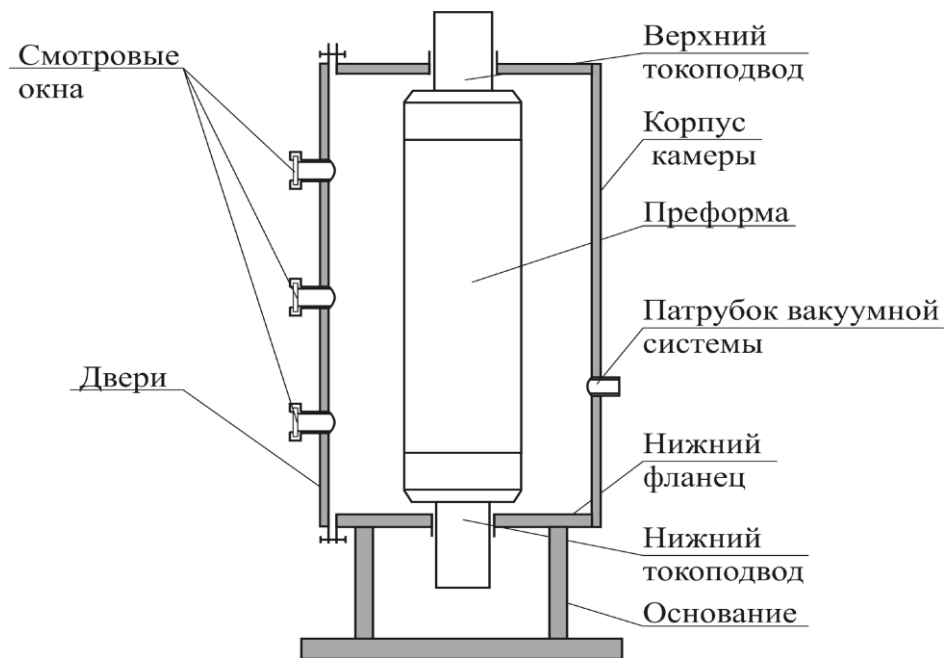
Принципова схема установки типу АГАТ-1.6
